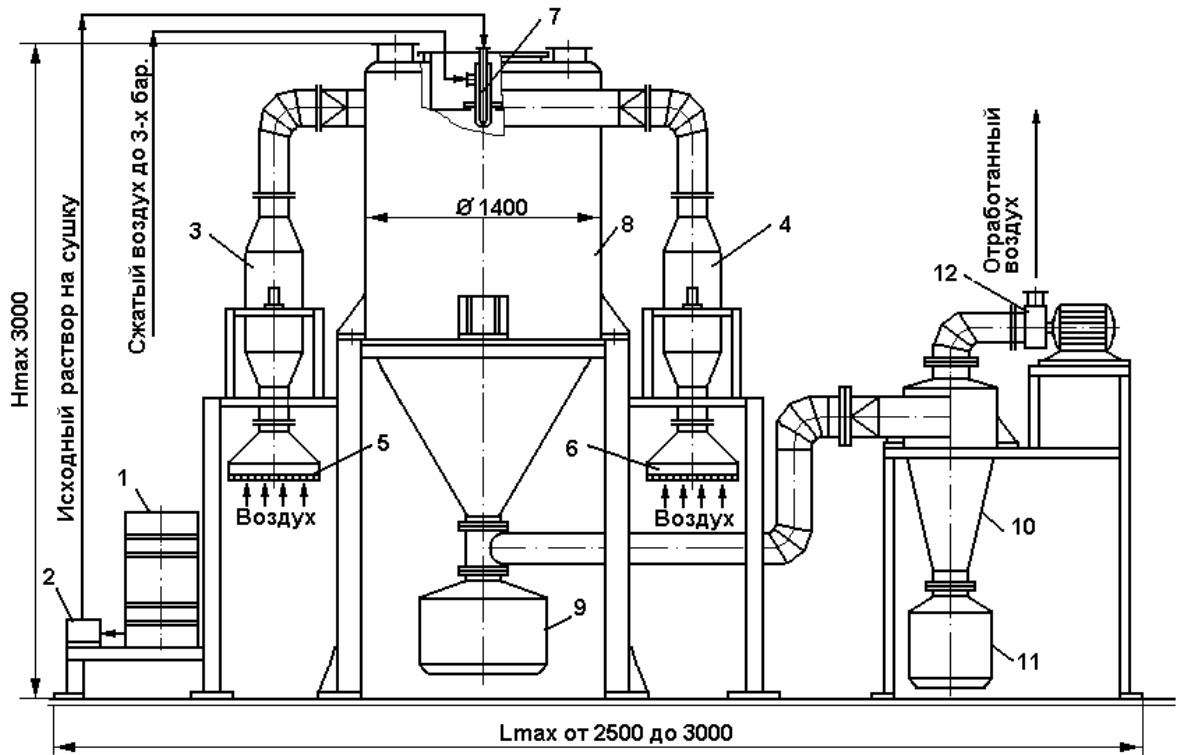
Принципиальная схема установки распылительной сушилки: 1-емкость для исходного раствора; 2-перистальтический насос; 3,4-электрокалориферы; 5,6-фильтры; 7-пневматическая форсунка; 8-сушильная камера; 9,11-сборники для сухого продукта; 10-циклон; 12-вытяжной ЦБ вентилятор.
